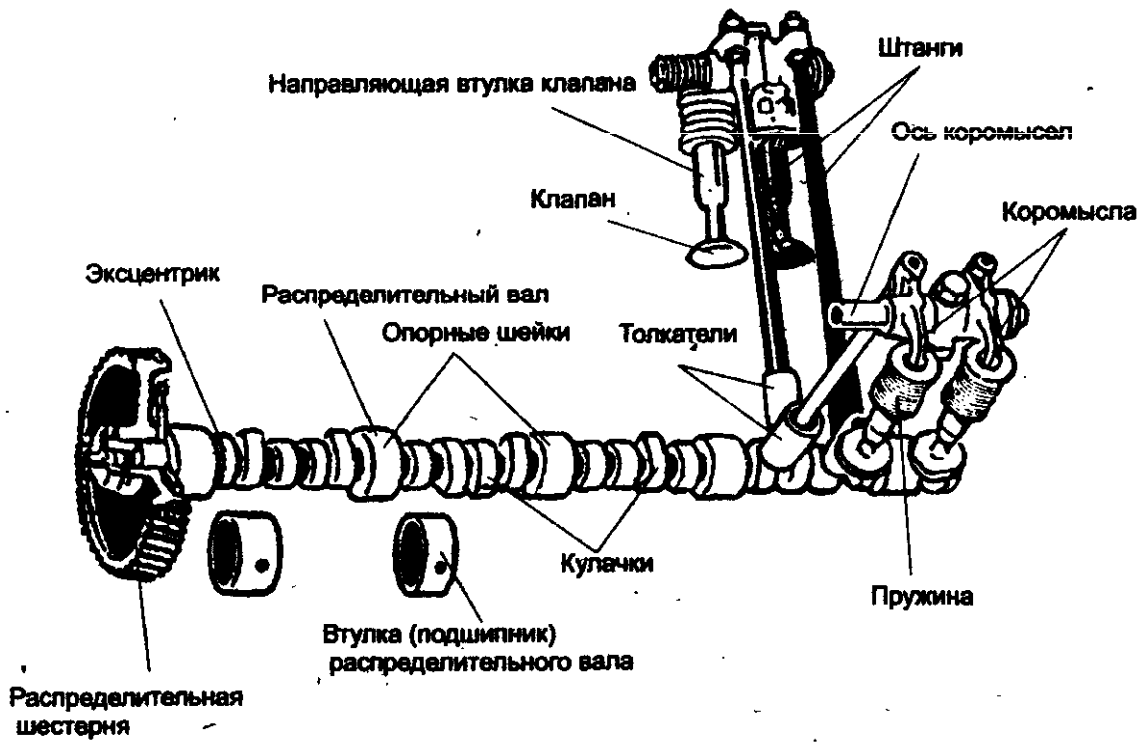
Газораспределительный механизм V-образного двигателя с верхним расположением клапанов
